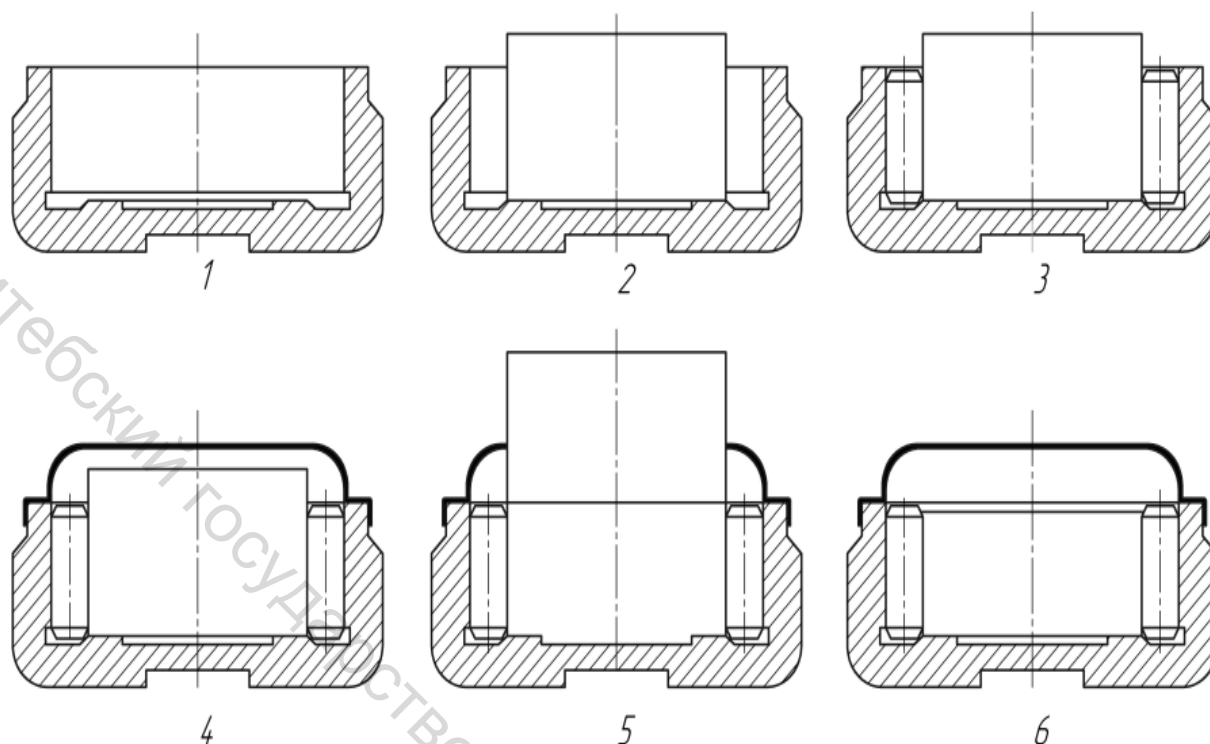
Схема сборки игольчатого подшипника:
